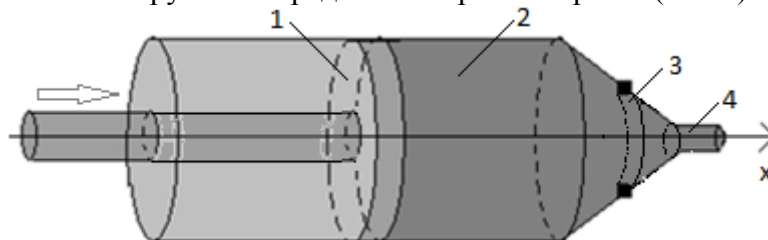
Схема прессования поршень-пресса 1- поршень, 2- керамическая масса, 3- формовочная насадка, 4- фильера.
